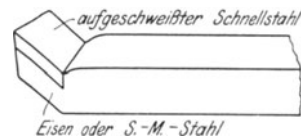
Aufschweißen von Schnellstahl auf Eisen oder S.-M.-Stahl.
